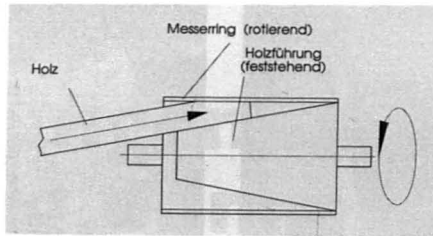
Zerspanungsprinzip Messerringzerspaner mit schräger Werkstoffzuführung (Fräsen mit kleinen Einstellwinkeln)
